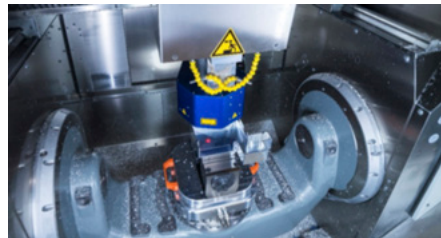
Inspektion einer typischen Fräsfläche durch HoloPort in einer Hermle C32U 5-Achsen-Fräsmaschine am Fraunhofer IPM
